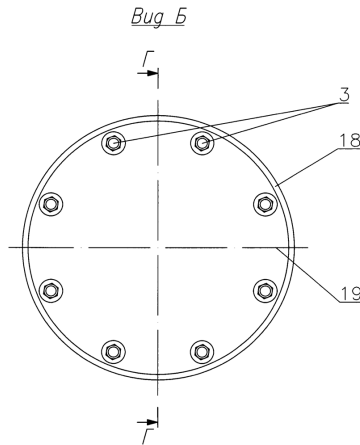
Взрывная камера, вид Б, сечение Г-Г [6], где: 3 – верхние упорные кольца; 18 – металлические кольца; 19 – прессующий диск.
